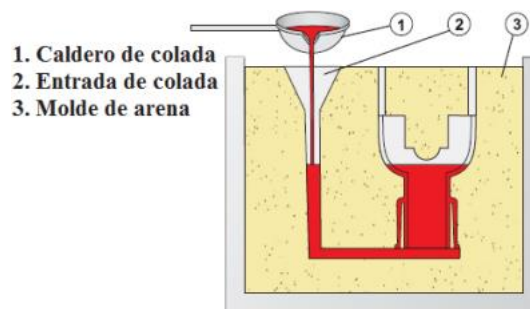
Fundición en molde desechable de arena aglutinada.
